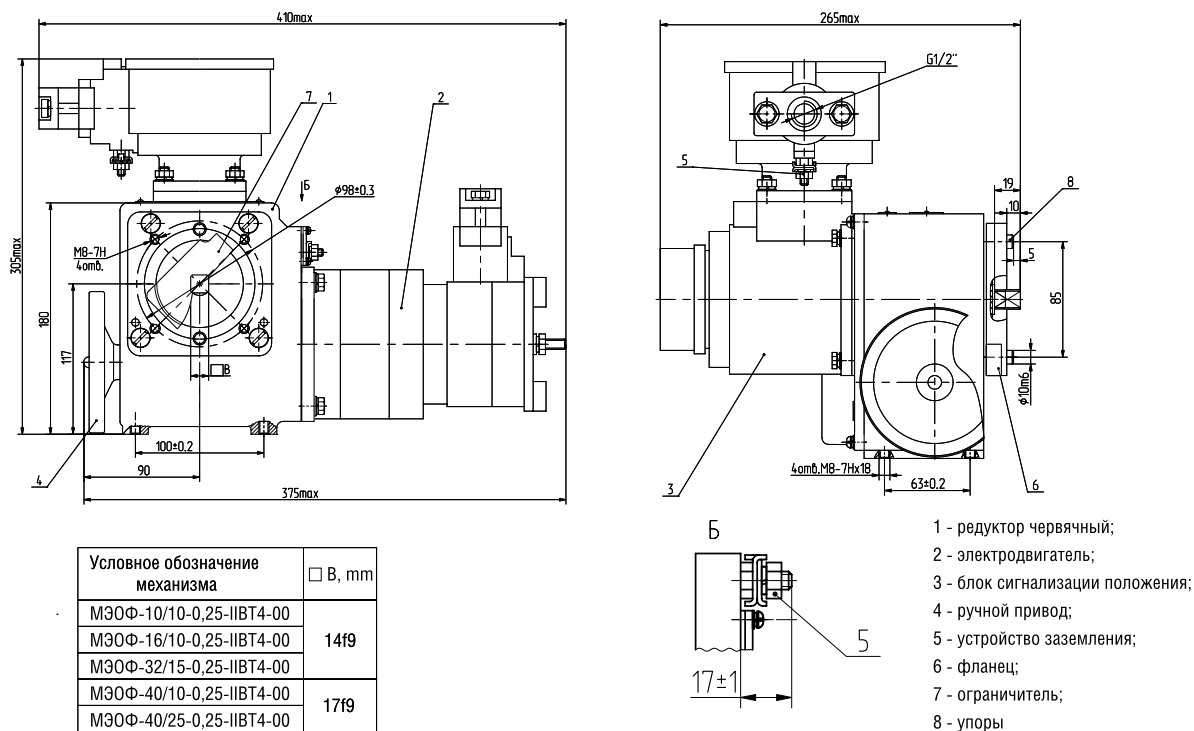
Габаритные и присоединительные размеры МЭОФ-40-IBT4
